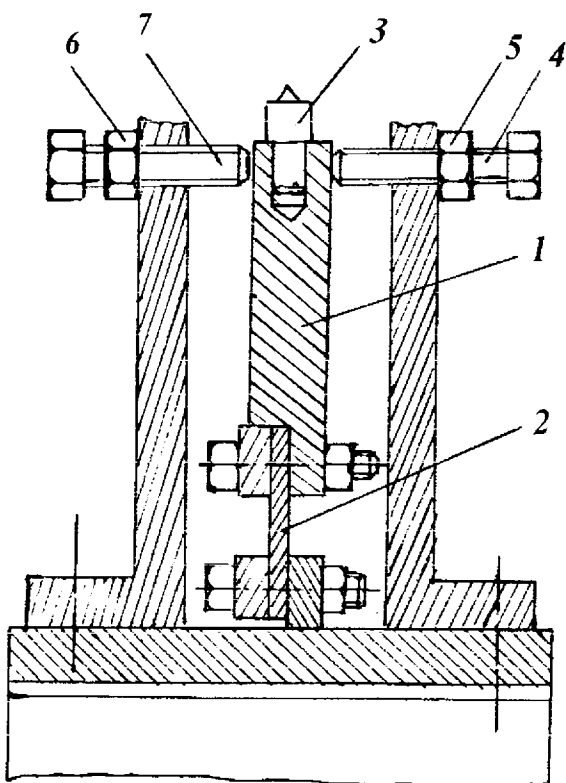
Приспособление для нанесения регулярного рельефа на круге
